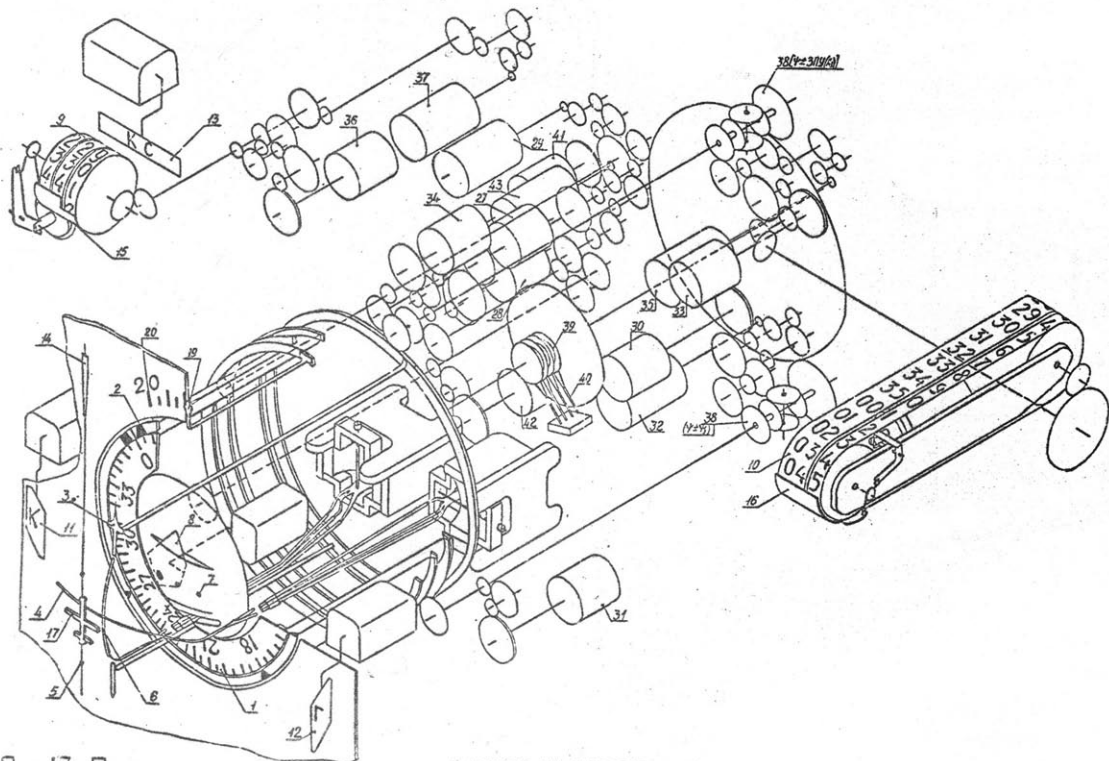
Прибор навигационный плановый ПНП-72-5М; ПНП-72-7
